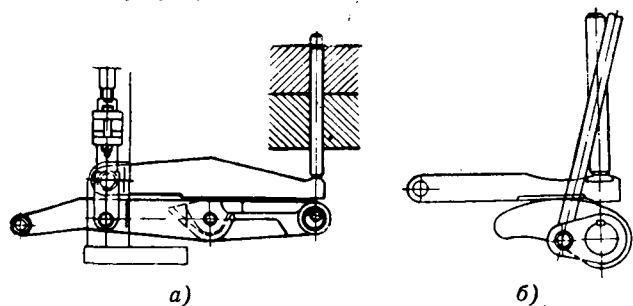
Нижний толкатель прессы с удлиненным рычагом для пневмоцилиндра и схема системы нижнего толкателя прессы.
